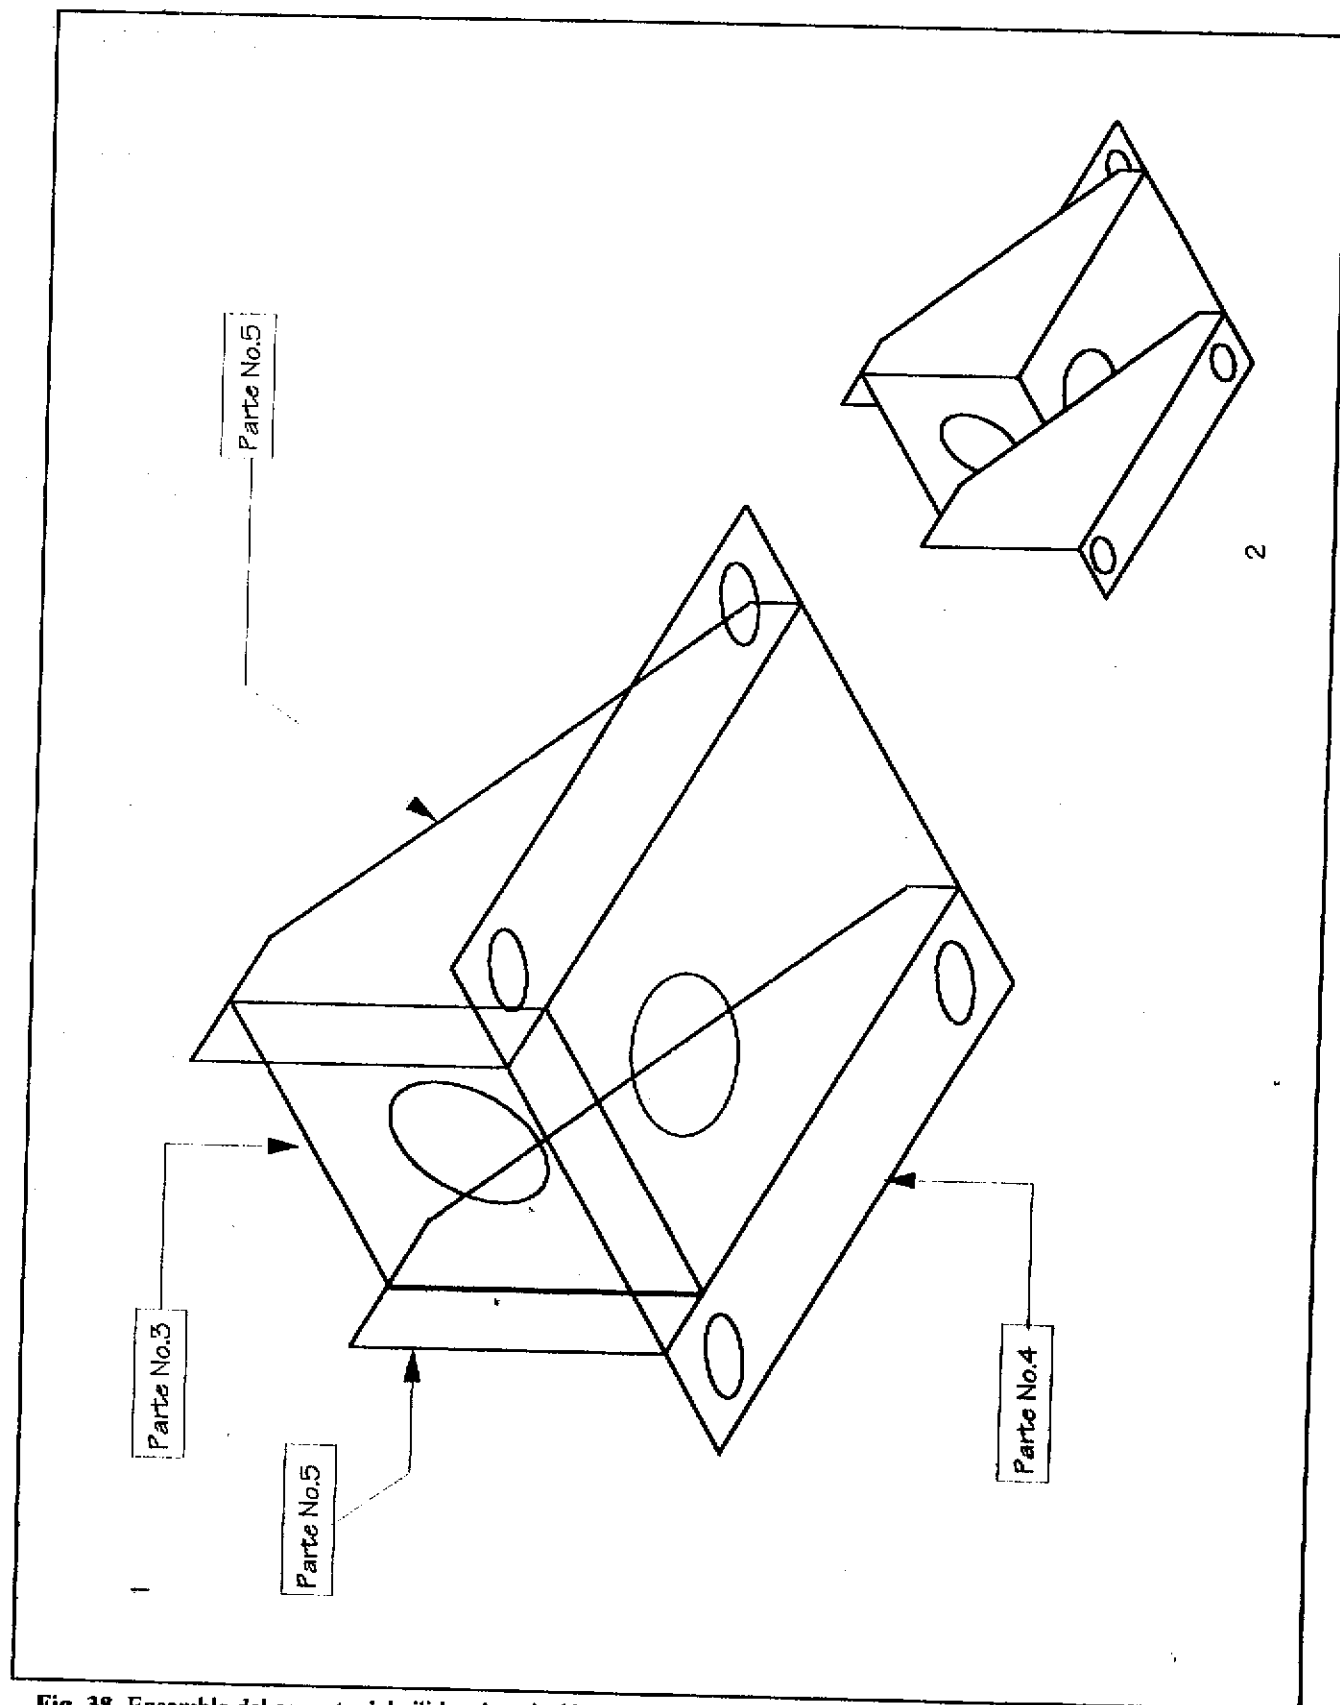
Ensamble del soporte del cilindro de sujeción.
